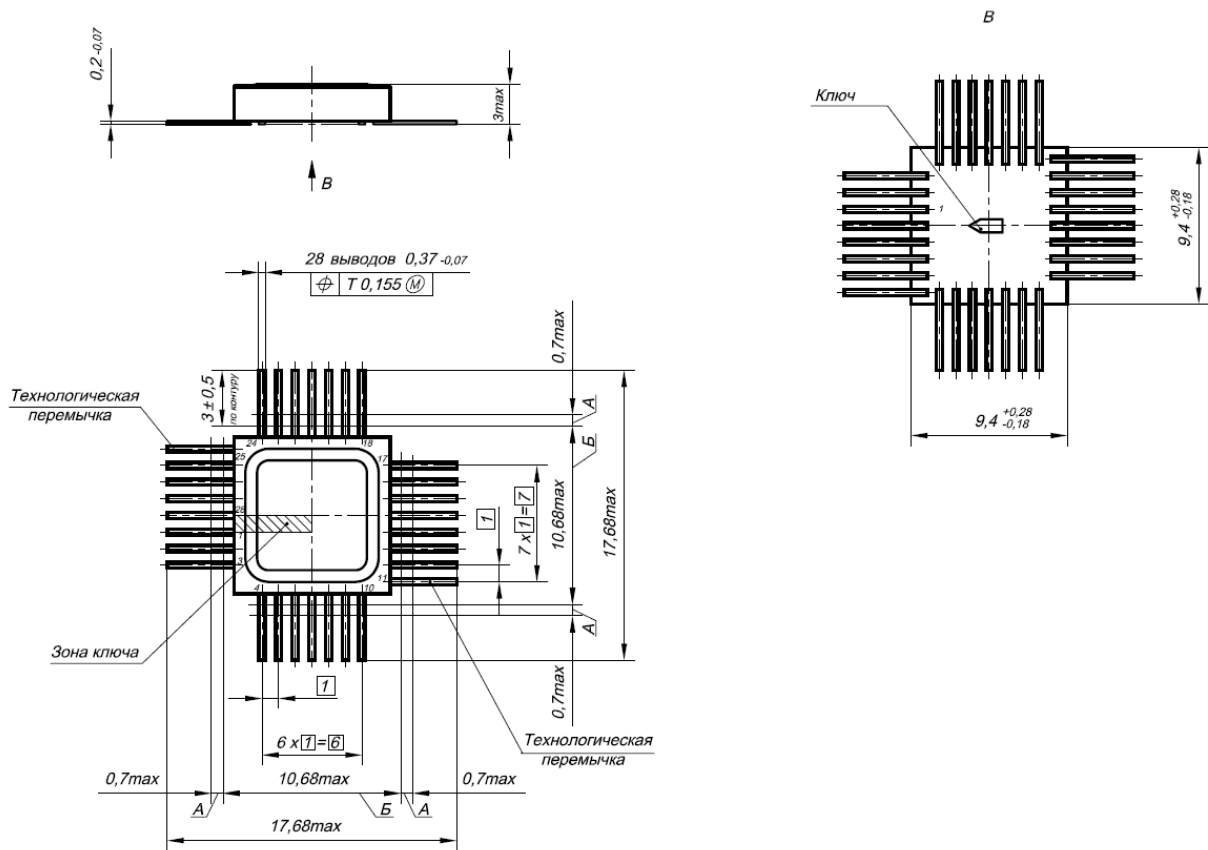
Габаритный чертеж корпуса Н09.28-1В, исполнение для микросхемы 5559ИН13У
